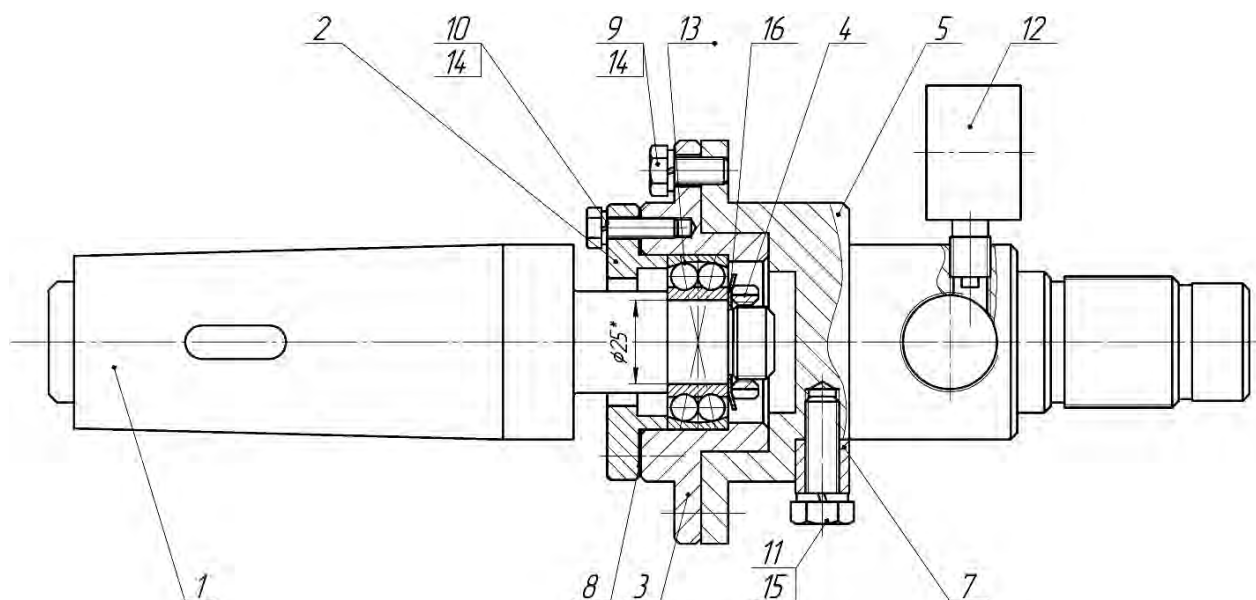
Конструктивная схема муфты для упрочняющей обработки пневмоударом
